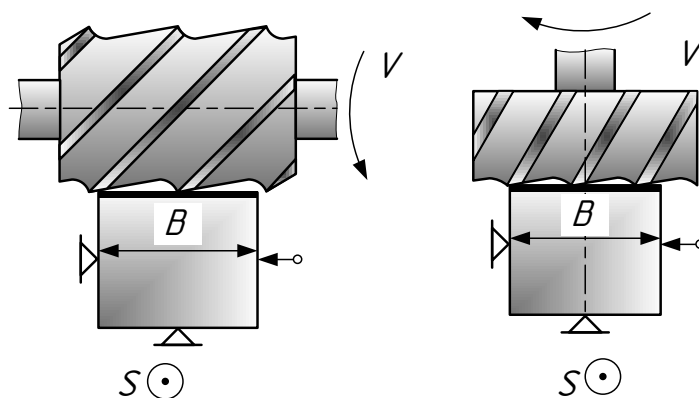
Обработка горизонтальной плоскости цилиндрической фрезой и торцевой фрезой
